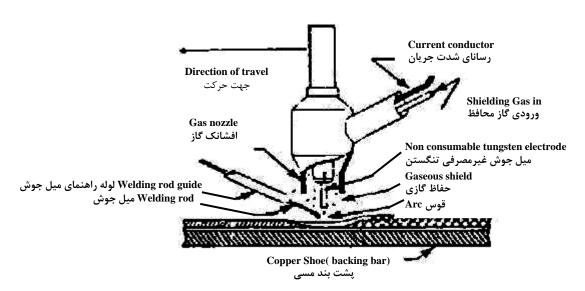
GAS TUNGSTEN ARC WELDING $-\Delta$ شکل $-\Delta$ جوشکاری قوسی با میل جوش تنگستن تحت گاز محافظ
